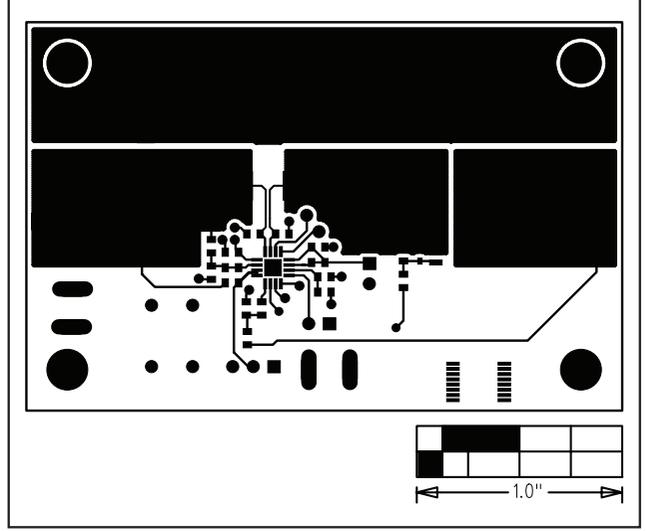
MAX4211E 评估板 PCB 布局 — 元件层
